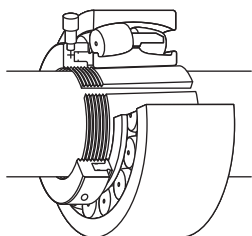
Tuerca hidráulica que se utiliza para montar el rodamiento sobre un manguito de tracción.
